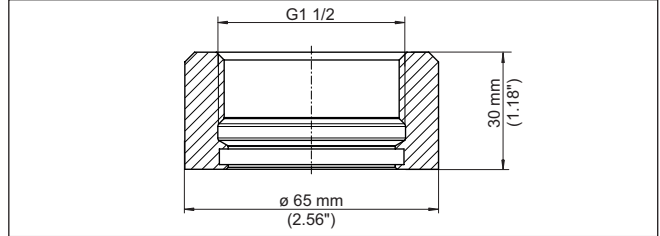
Maße Einschweißstutzen Gewinde G1½ (ISO 228-1) - Hygienedesign
